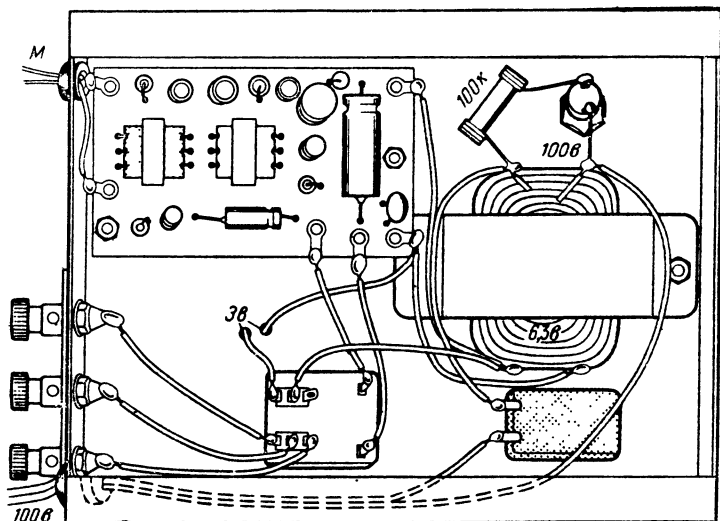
Размещение узлов и деталей схемы в корпусе.
